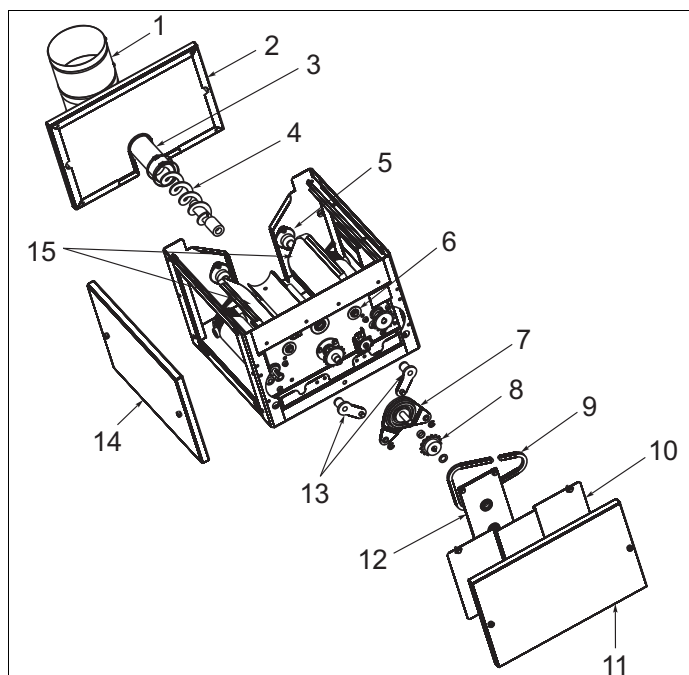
Désassemblage des pales d'agitateur 300 et 600
